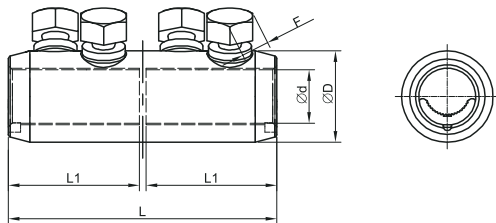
Внешний вид и габаритные размеры гильз до 1 кВ и до 35 кВ /
